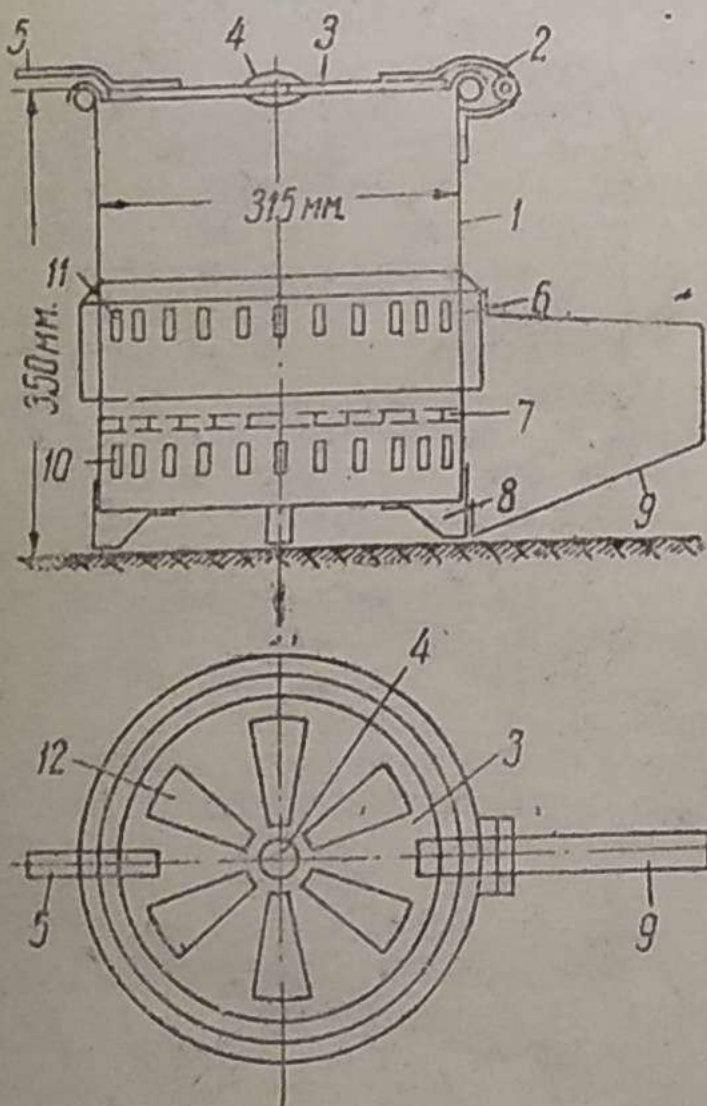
Конструкция нагревательной печи для обогрева двигателя горячими газами, получаемыми при горении древесного угля:
